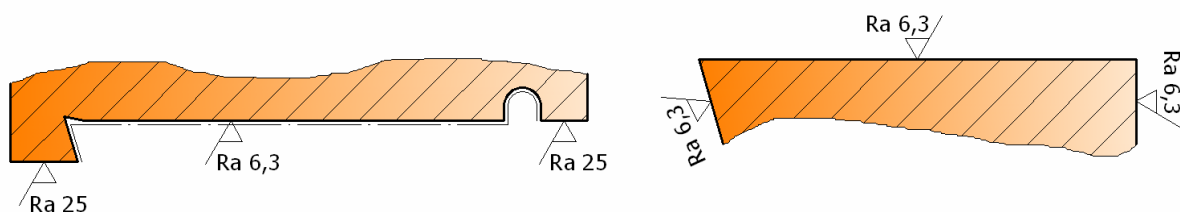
Geometrické a rozměrové tolerance složeného kola
